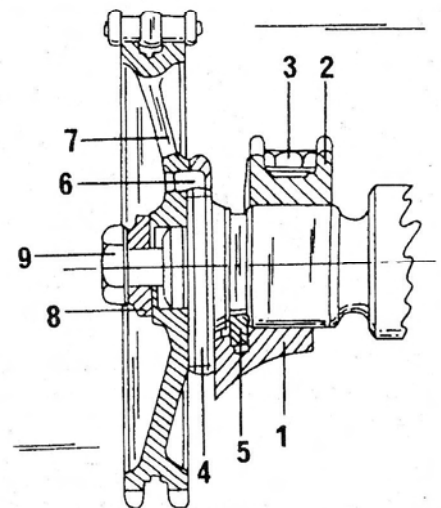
Разрез распределительного вала и его крепление в головке цилиндров.
